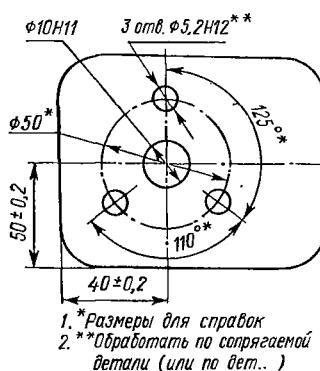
Нанесение размеров элементов детали, подлежащих обработке по другой детали
